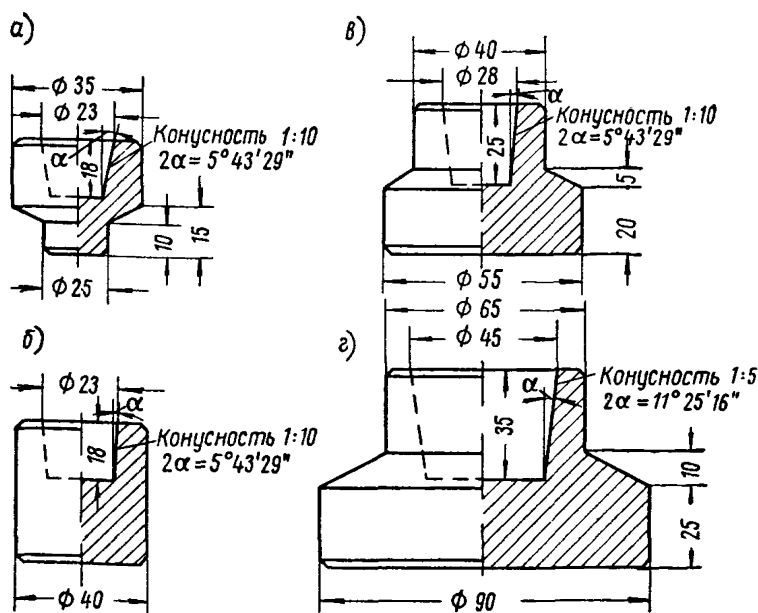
Конструкция и типоразмеры электродов, которые рекомендуется изготовлять холодным прессованием
